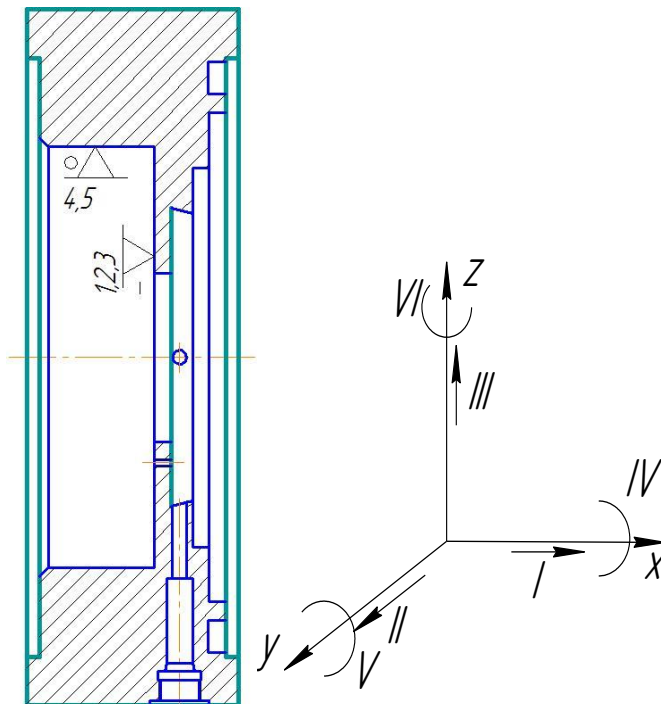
Схема базування заготовки на токарній з ЧПК операції
